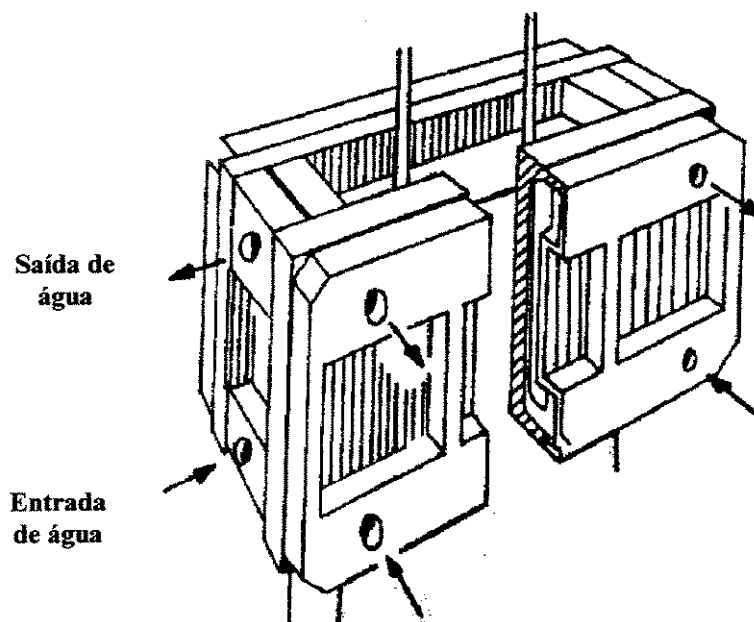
Detalhe do molde de lingotamento contínuo de placas^[17].
